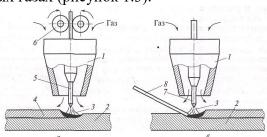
Схема дуговой сварки в среде защитных газов плавящимся (а) и неплавящимся (б) электродами: 1 – сопло горелки; 2 – свариваемая деталь; 3 – дуга; 4 – сварной шов; 5, 7 – плавящийся и неплавящийся (вольфрамовый) электроды; 6 – подающий механизм; 8 – присадочный материал
